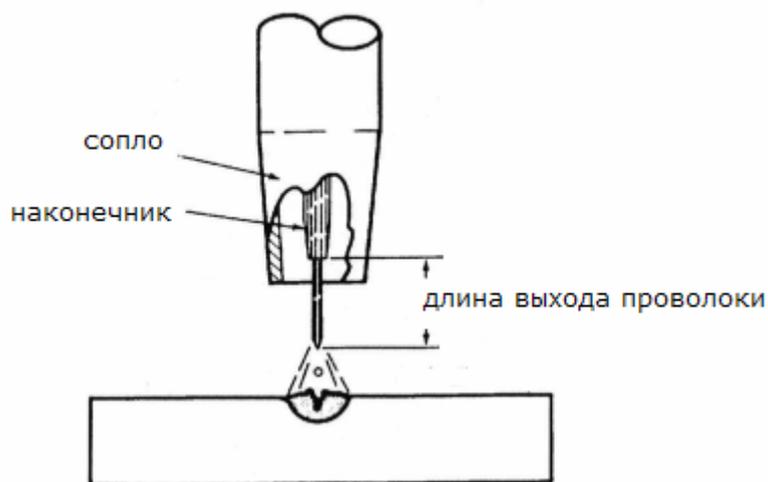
Расположение сварочной проволоки перед началом сварки
